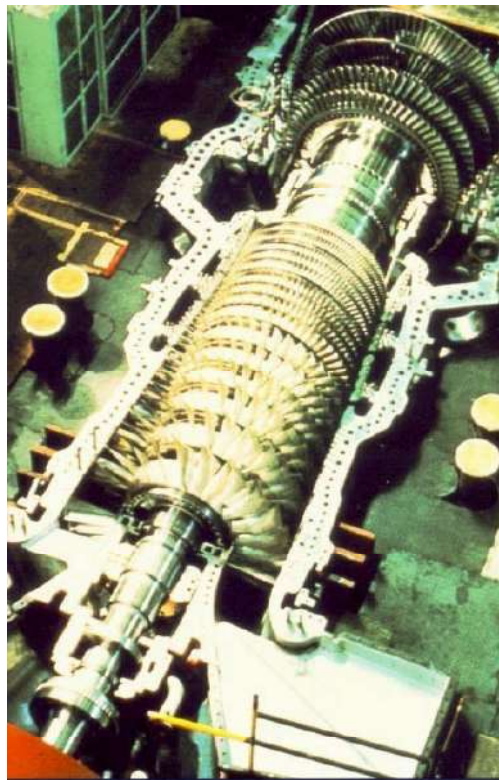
Vista de Turbina WESTINGHOUSE em Montagem
